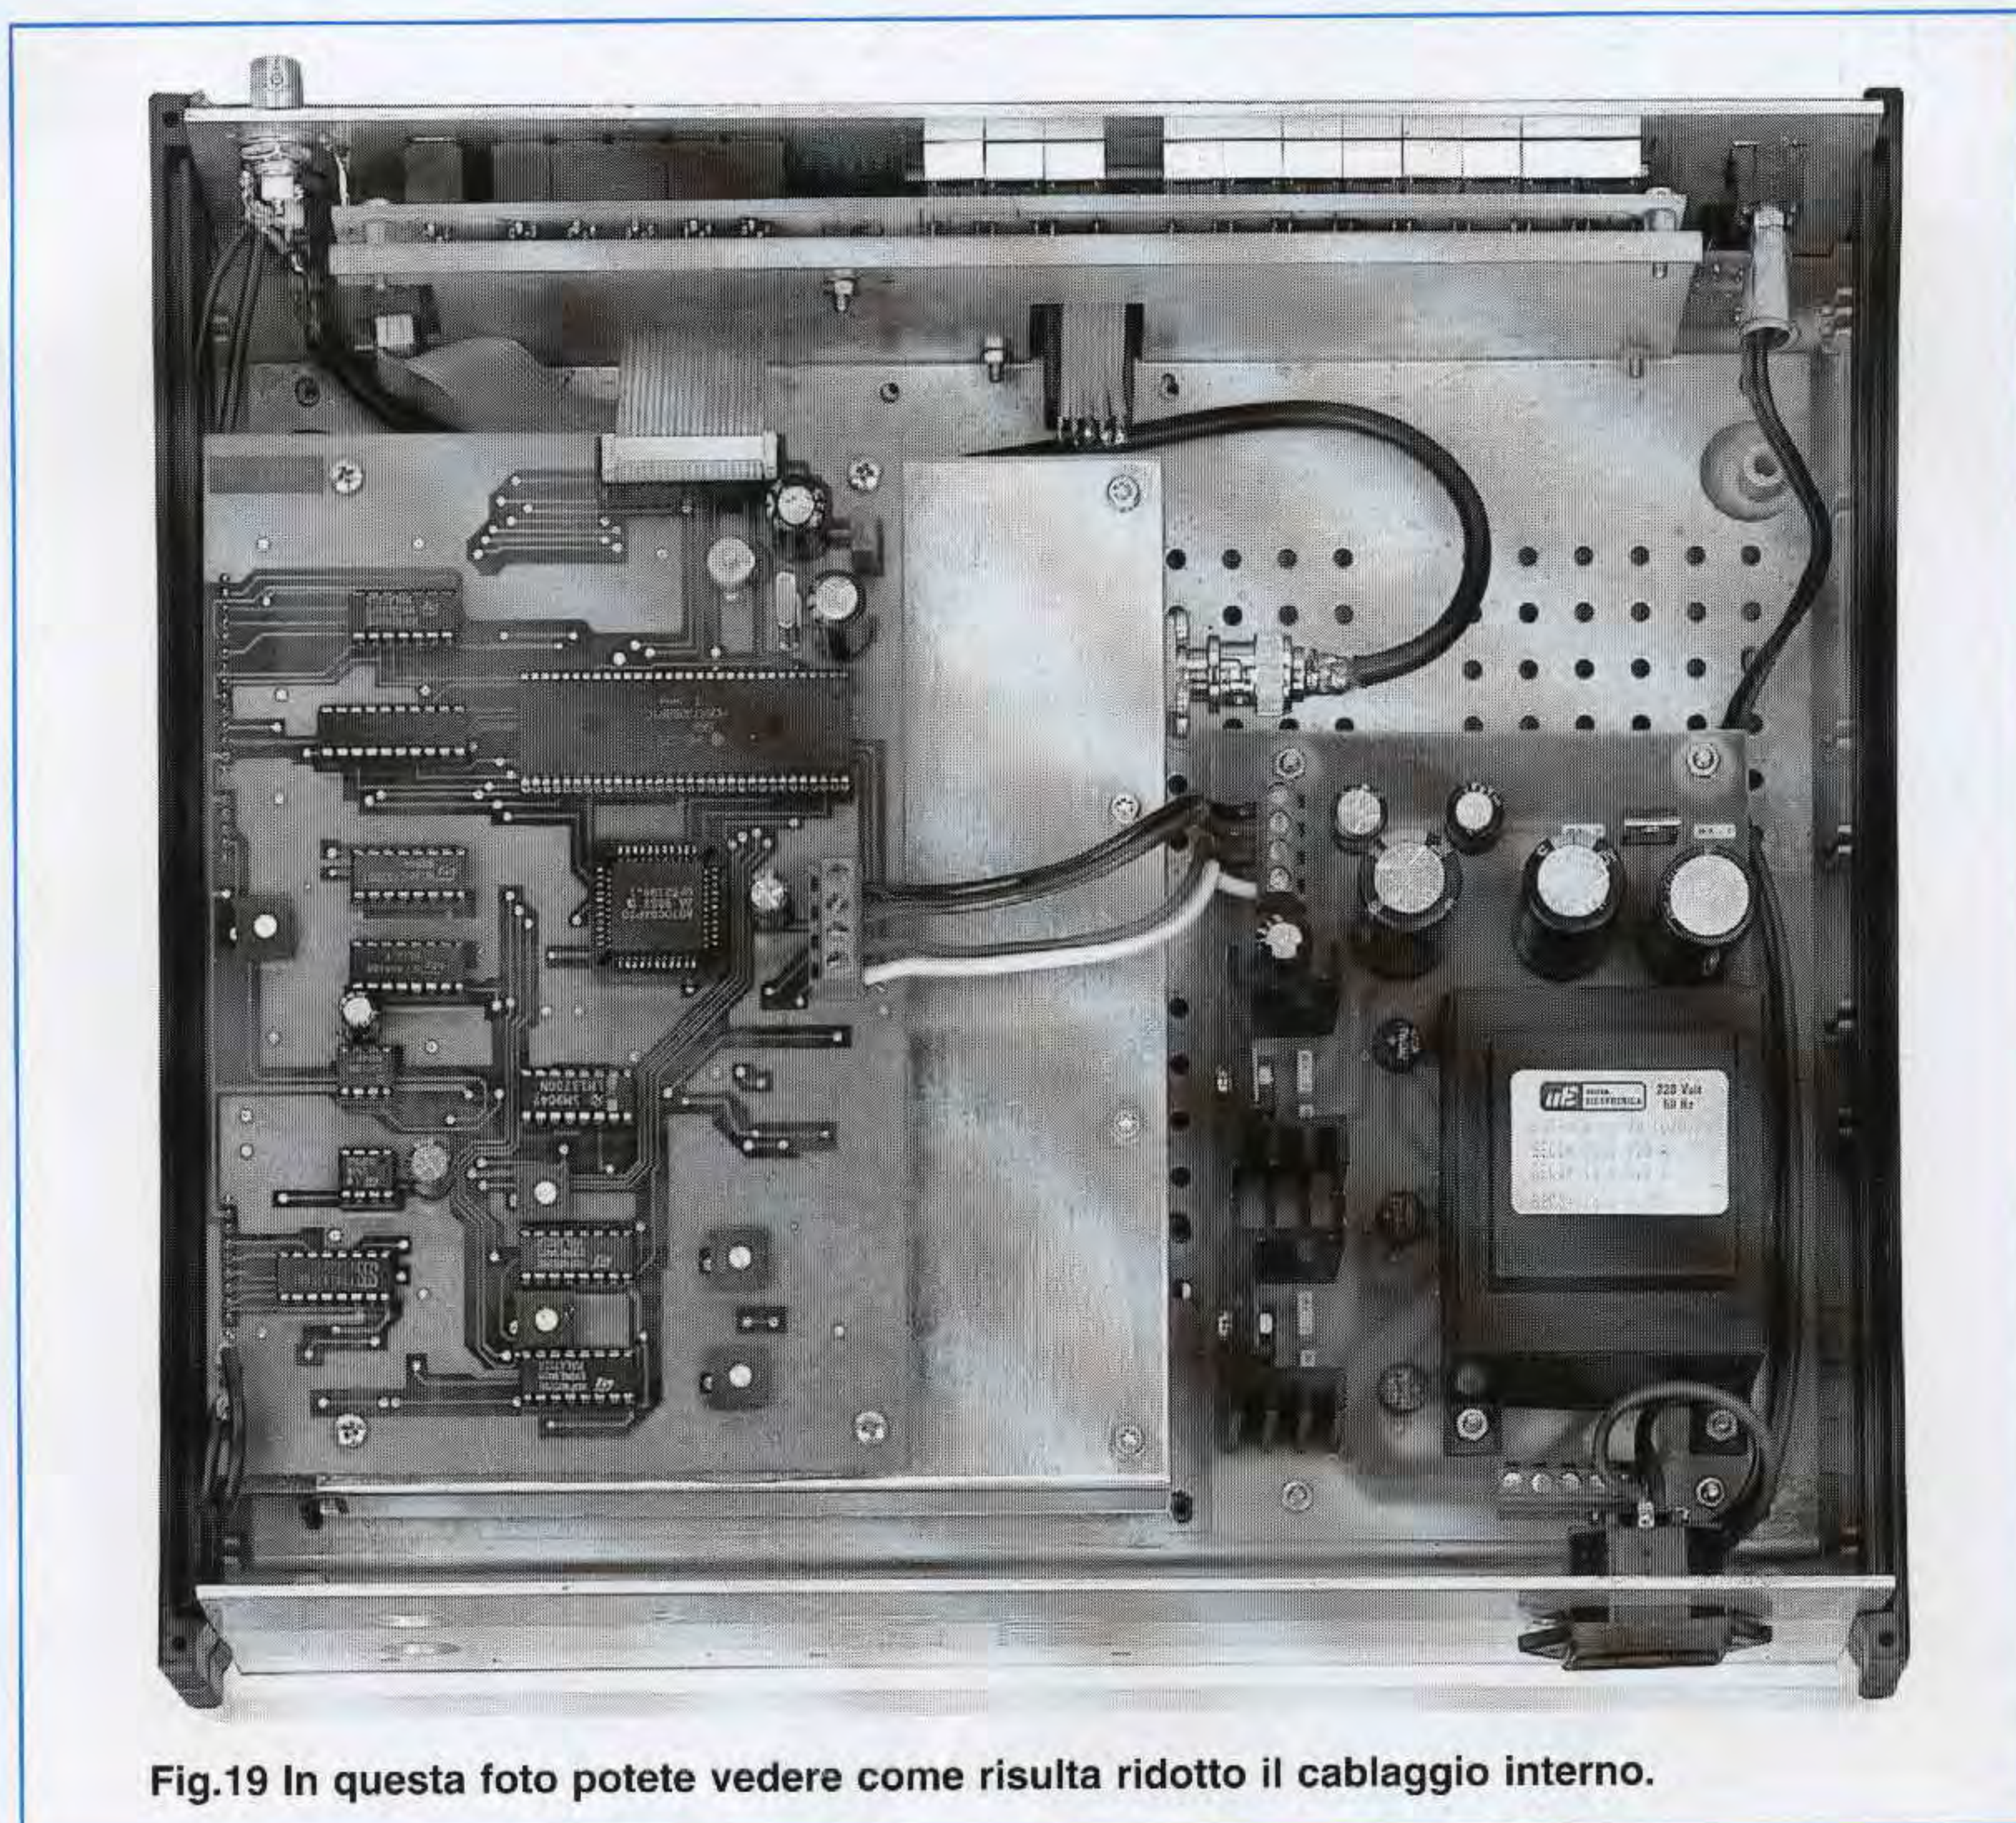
In questa foto potete vedere come risulta ridotto il cablaggio interno.
